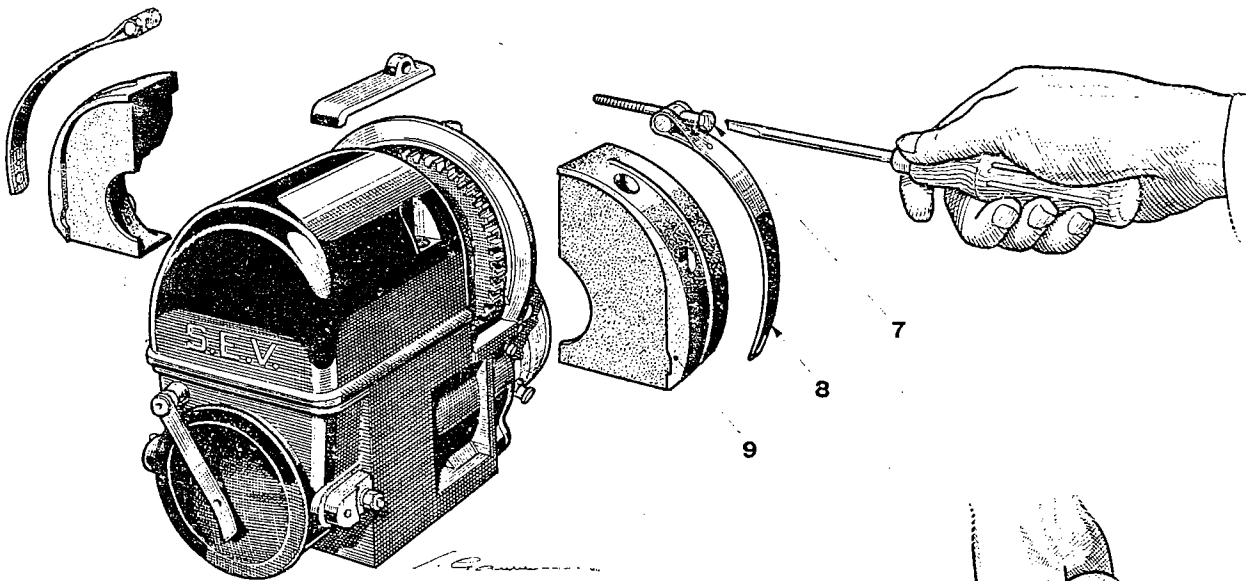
DÉMONTAGE DU DISTRIBUTEUR
